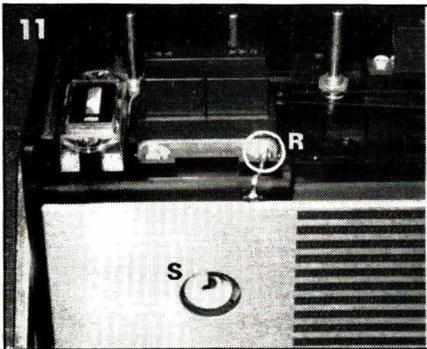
dessouder la connexion de masse de la cosse R. La laisser soudée du côté du panneau avant.
